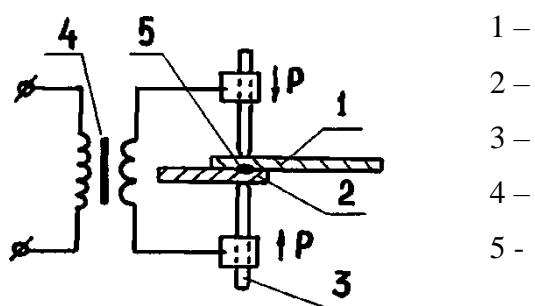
Принципиальная схема точечной сварки
